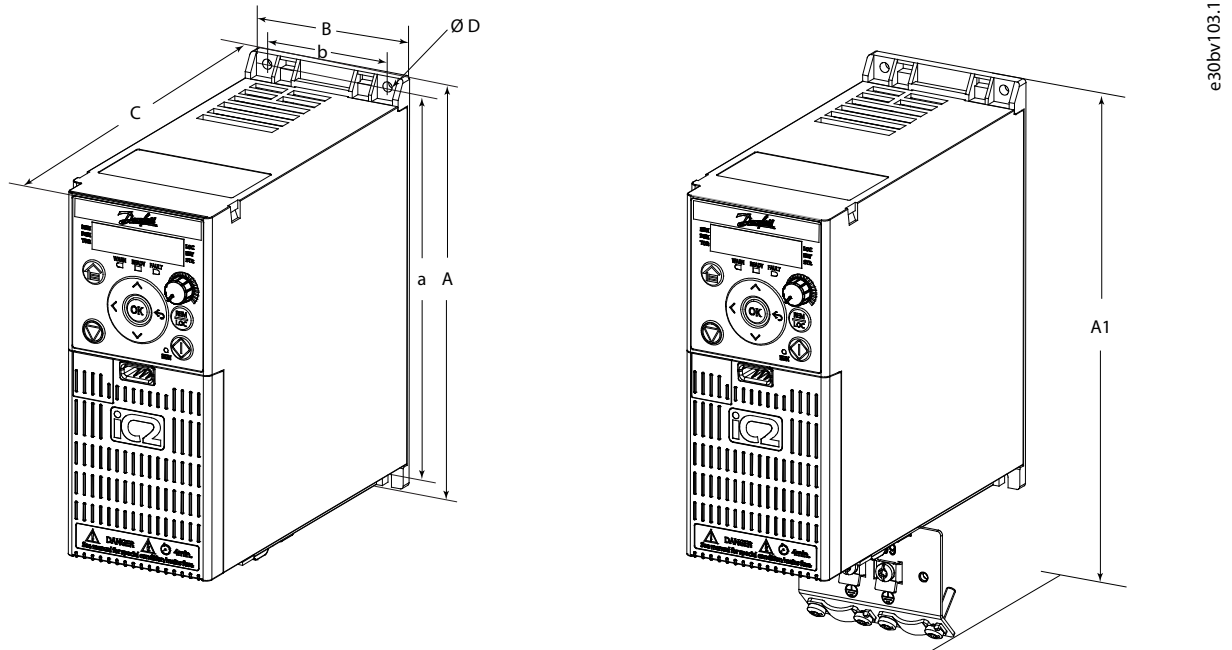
Tailles et dimensions protection IP20/type ouvert
